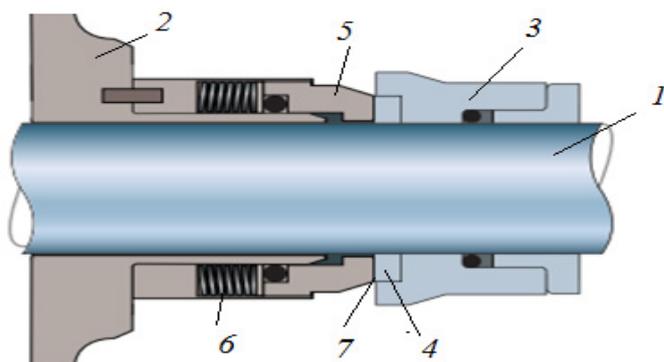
Схема торцевого уплотнения: 1 – вал насоса; 2 – корпус насоса; 3 – гильза; 4 – вращающееся уплотнительное кольцо; 5 – неподвижное уплотнительное кольцо; 6 – пружина, 7 – зазор между кольцами
